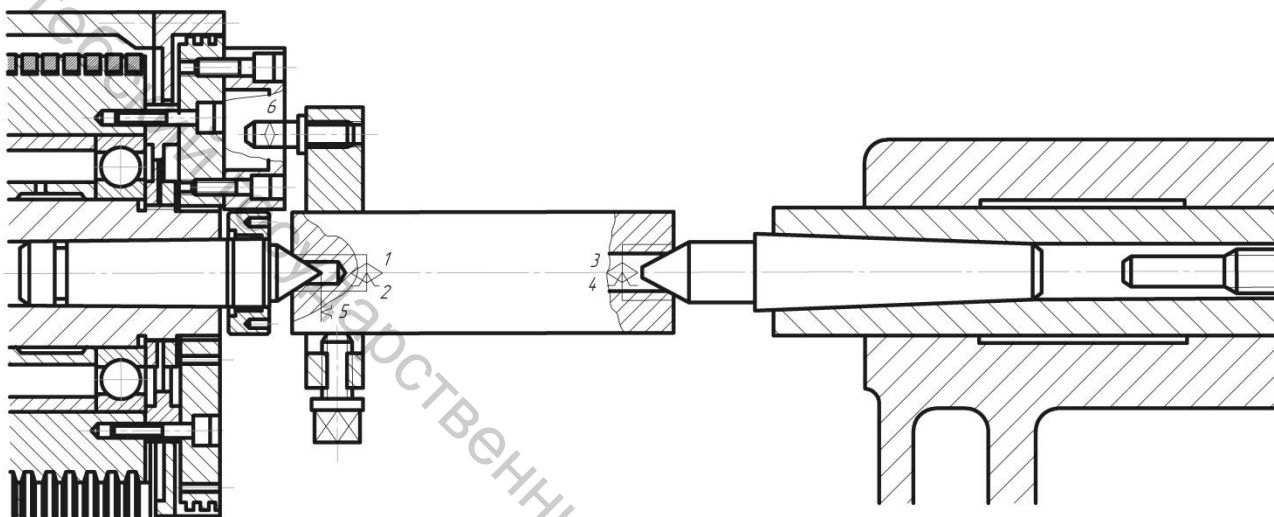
Пример установки заготовки на круглошлифовальном станке в невращающихся центрах с использованием специального поводка
